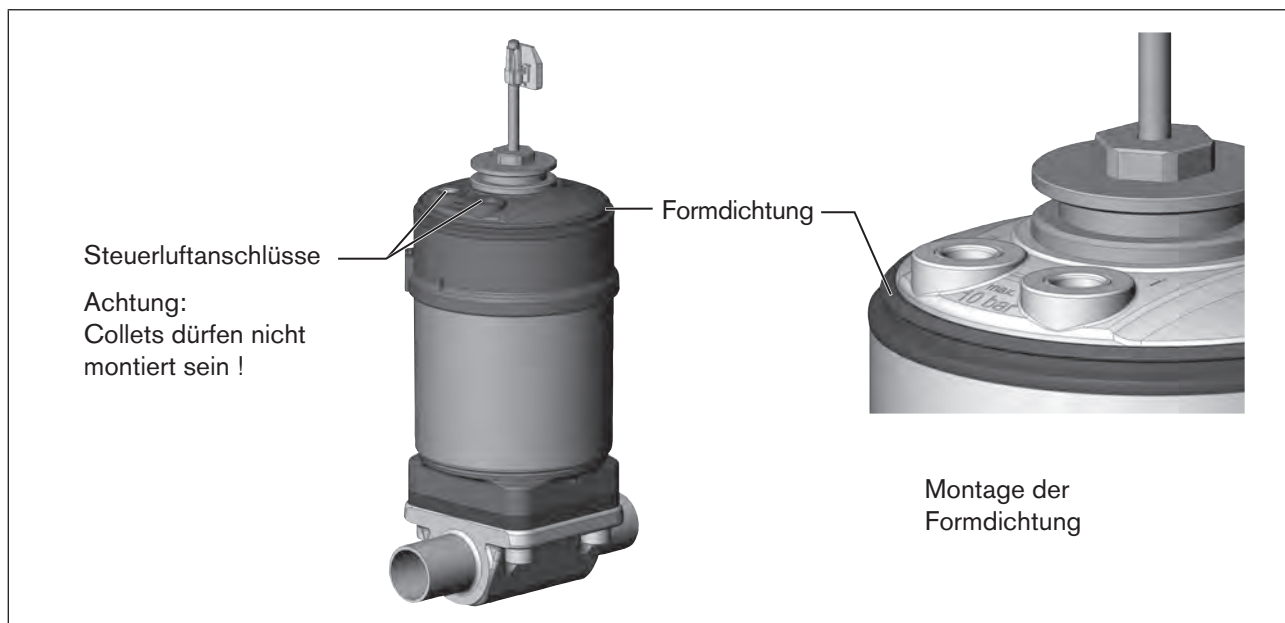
Montage der Dichtringe, Reihe 2103, 2300 und 2301
